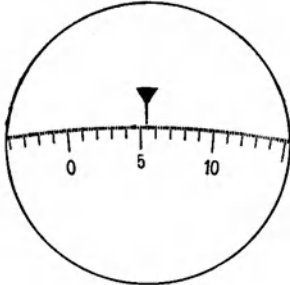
Optischer Winkelmesser. Gesichtsfeld.
